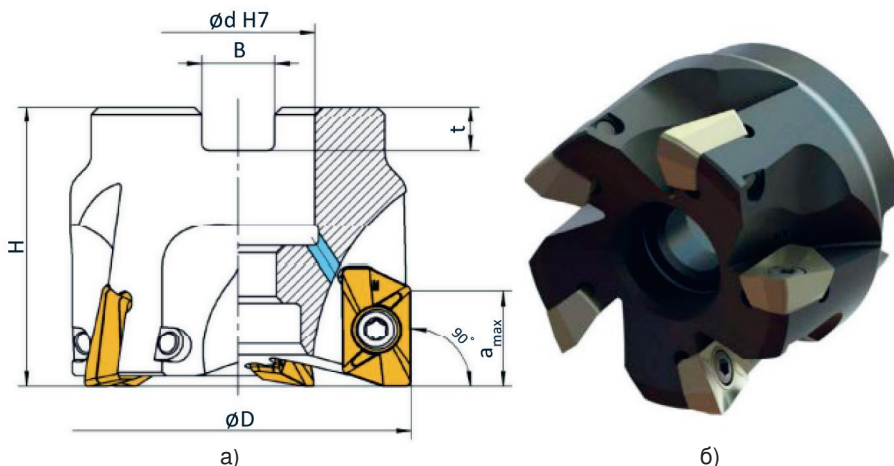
Конструктивные особенности (а) и внешний вид (б) торцевой фрезы мод. 218-050A16
